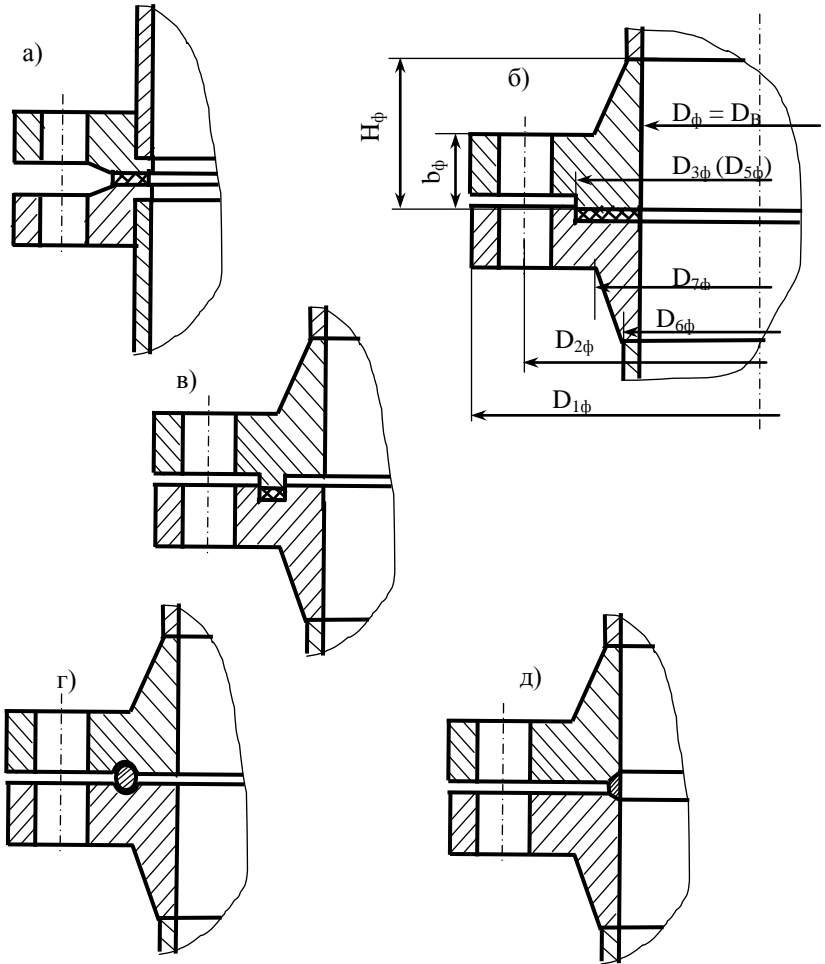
Форма привалочной поверхности фланцев: а) гладкая (с соединительным выступом); б) выступ-впадина; в) шип-паз; г) под шлифованное кольцо овального сечения; д) коническая под линзовое уплотнение
